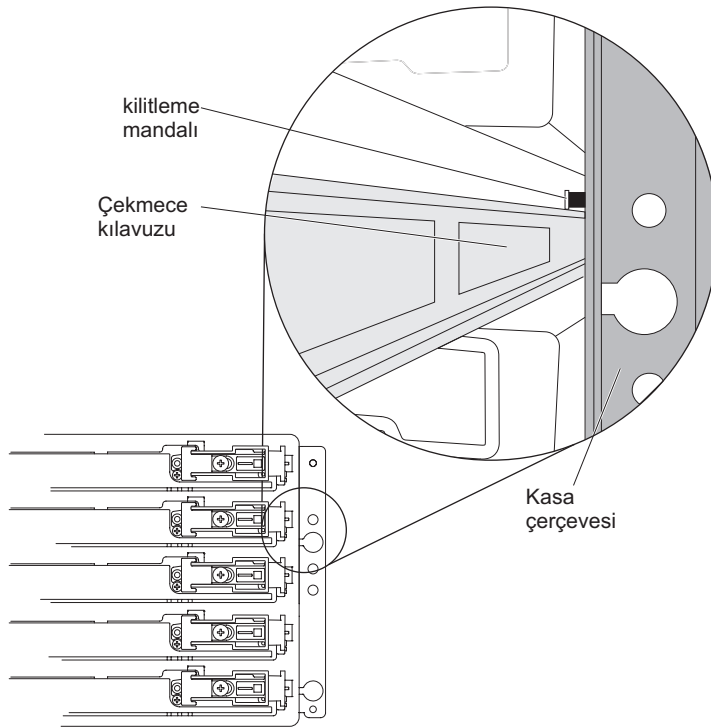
Sürücü çekmecesinin kenarındaki sürücü çekmecesini serbest bırakma kolu
